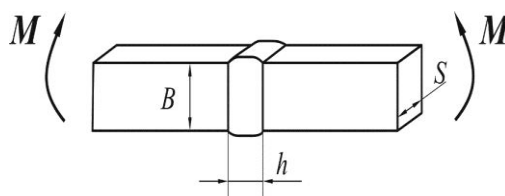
Расчетная схема изгиба стыкового сварного соединения с мягкой прослойкой
